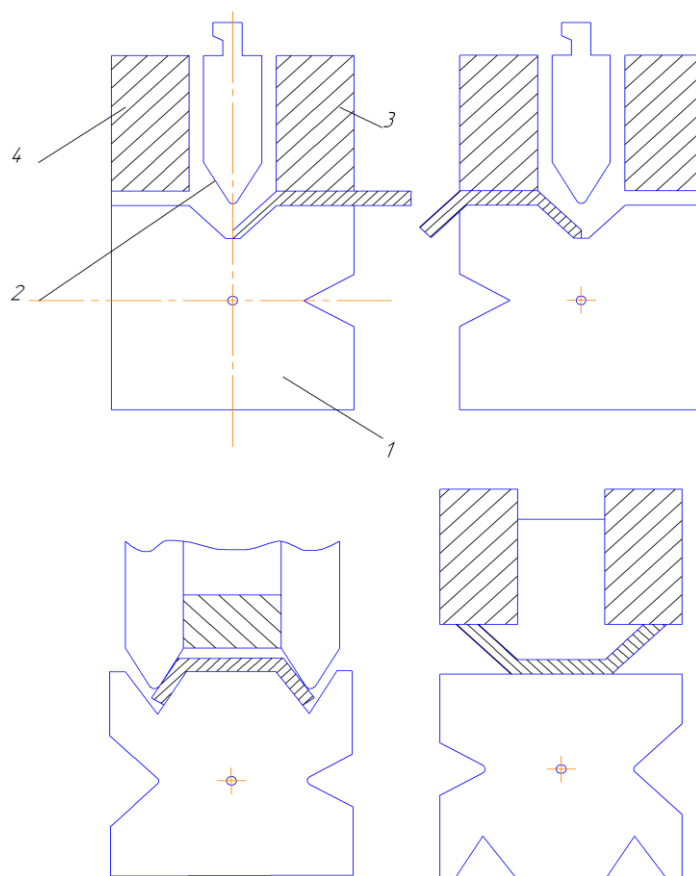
Універсальний комплект інструментів для згинання
